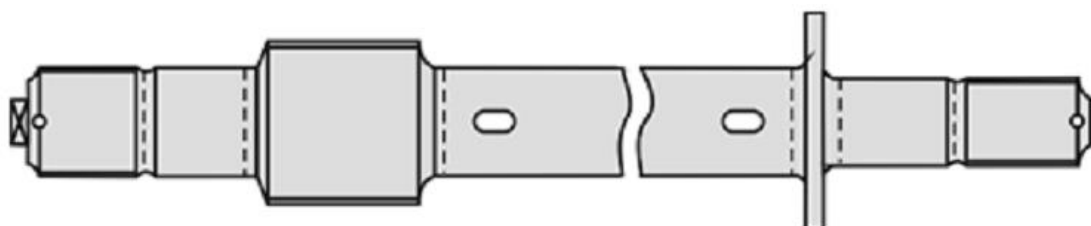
Схема кругового сканирования тяги поводка
